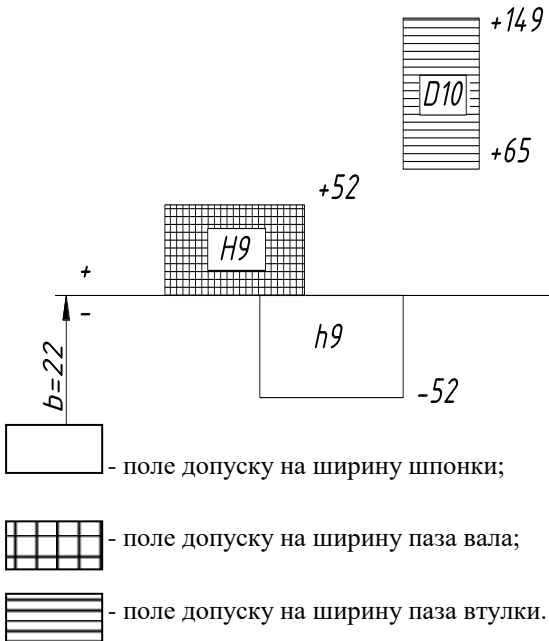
Схема розташування полів допусків шпонкового з'єднання
